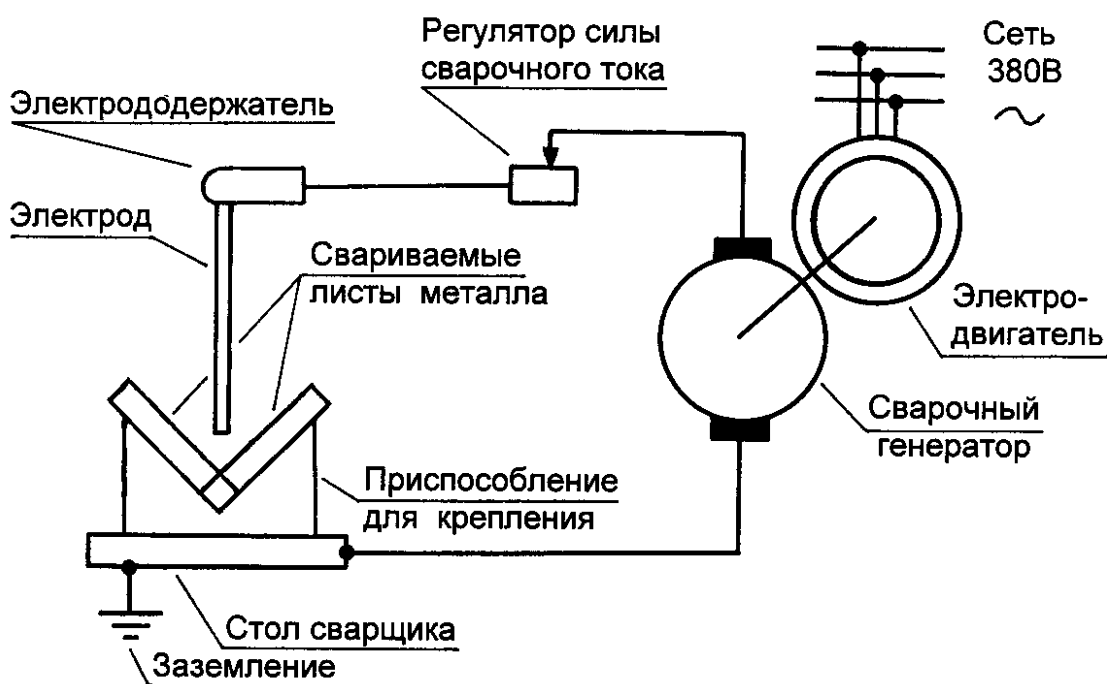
Принципиальная схема сварки постоянным током
